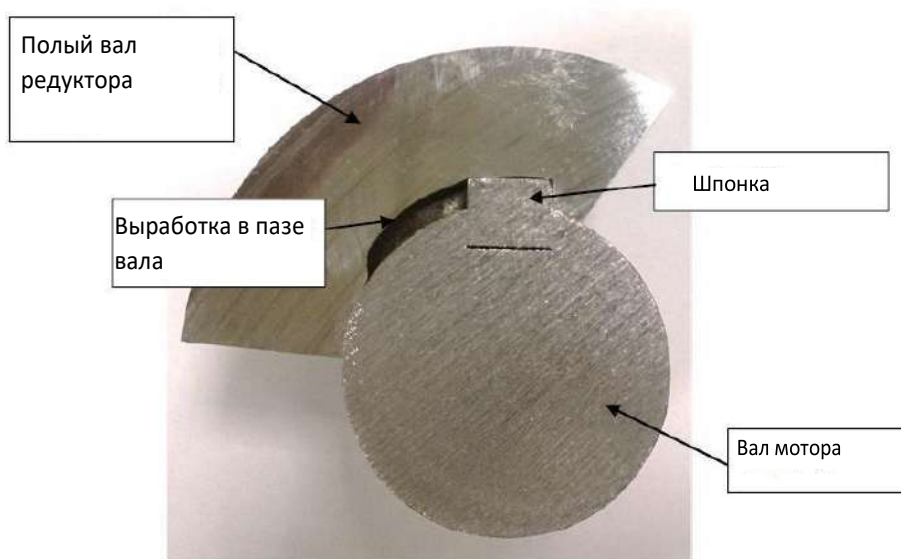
Вид поврежденного впалого вала редуктора в разрезе
